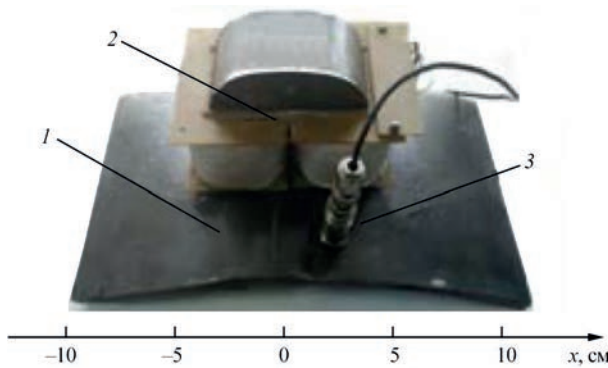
Розташування НЕМ на фрагменті труби з повздовжнім зварним з'єднанням: 1 – фрагмент труби; 2 – НЕМ; 3 – перетворювач акустичної емісії
